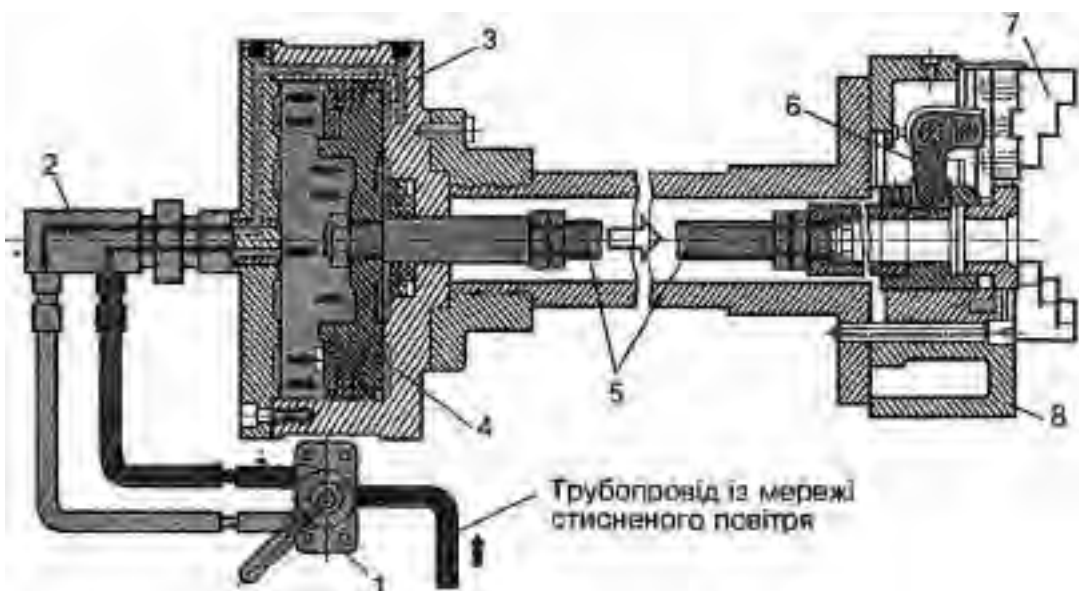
ПНЕВМАТИЧНИЙ ТОКАРНИЙ ПАТРОН
